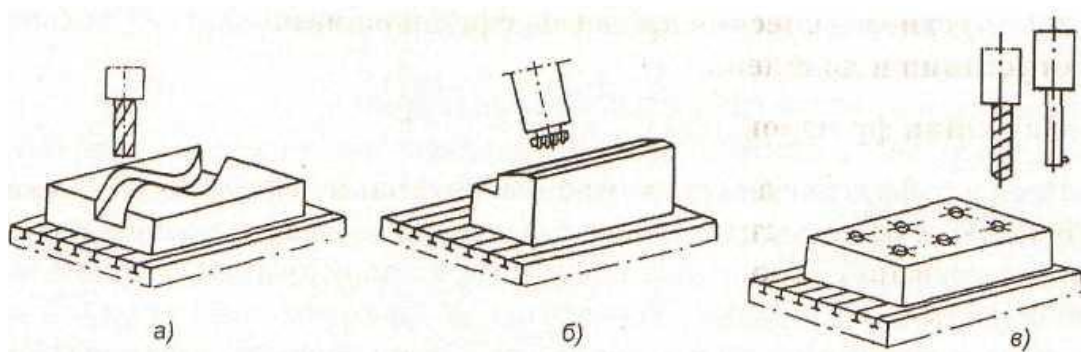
Схемы обработки заготовок на продольно-фрезерных станках
